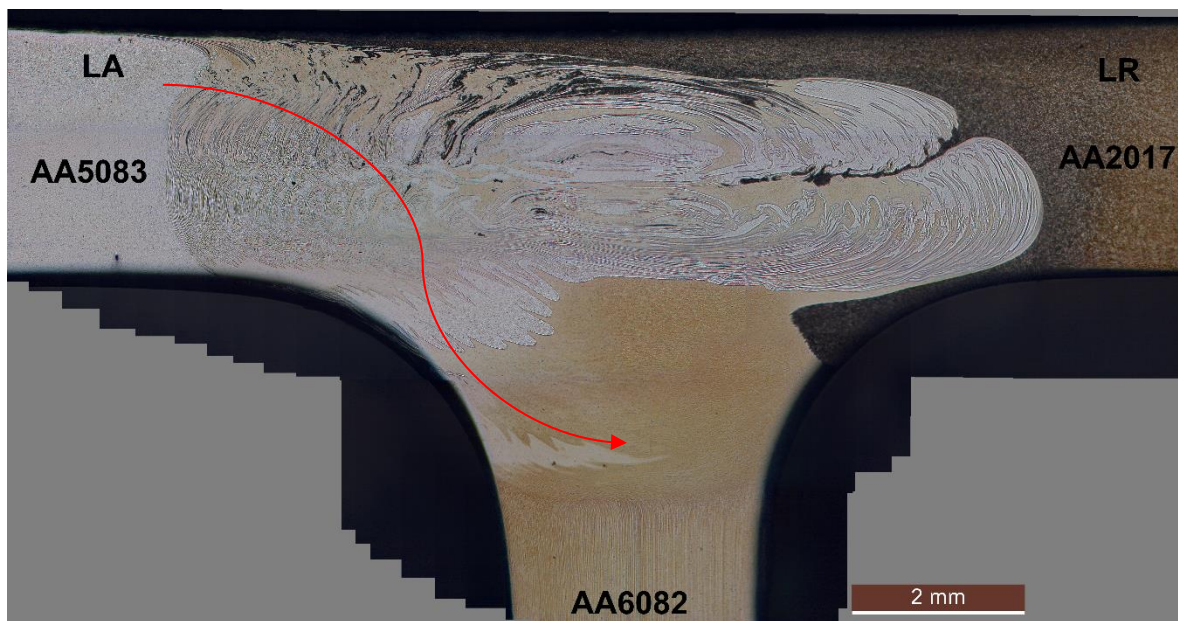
Macrografia da soldadura 562BRP-4
